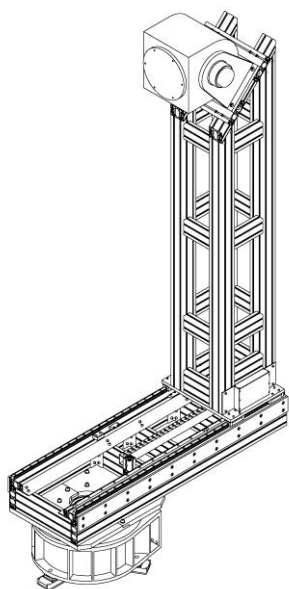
Общий вид четырехкоординатного опорно-поворотного устройства
